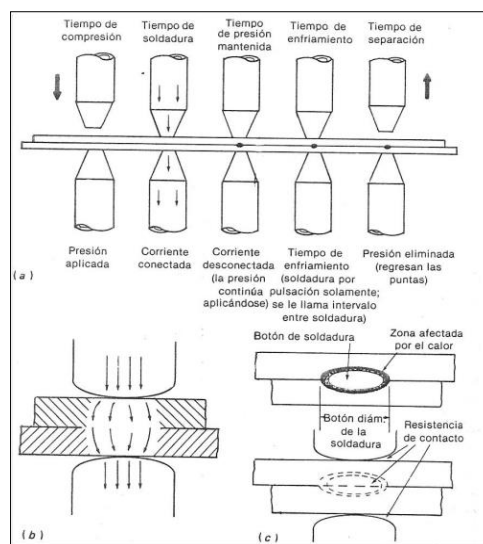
A) Secuencia gráfica durante la ejecución de una soldadura de puntos. B) Trayectoria de la corriente de soldadura en una soldadura por puntos. C) Zona afectada por el calor en relación con el botón de soldadura.
